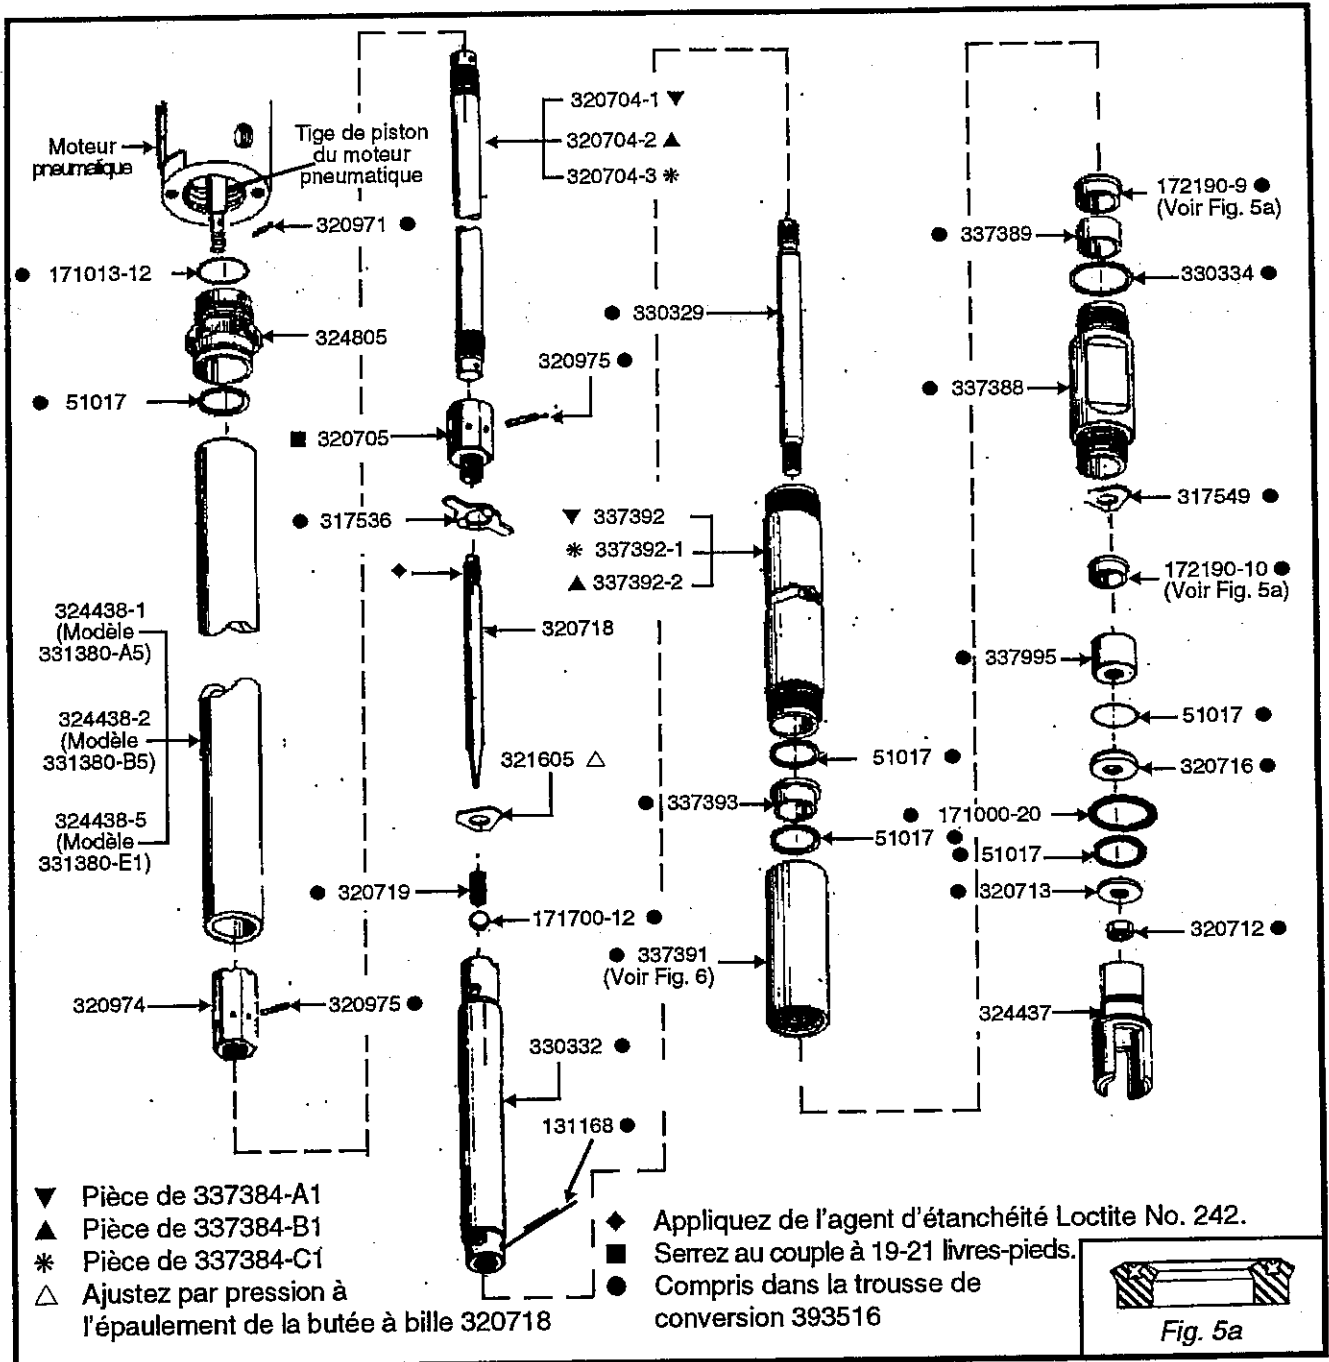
Réassemblage du tube de pompe 337384-A1, 337384-B1 ou 337384-C1
